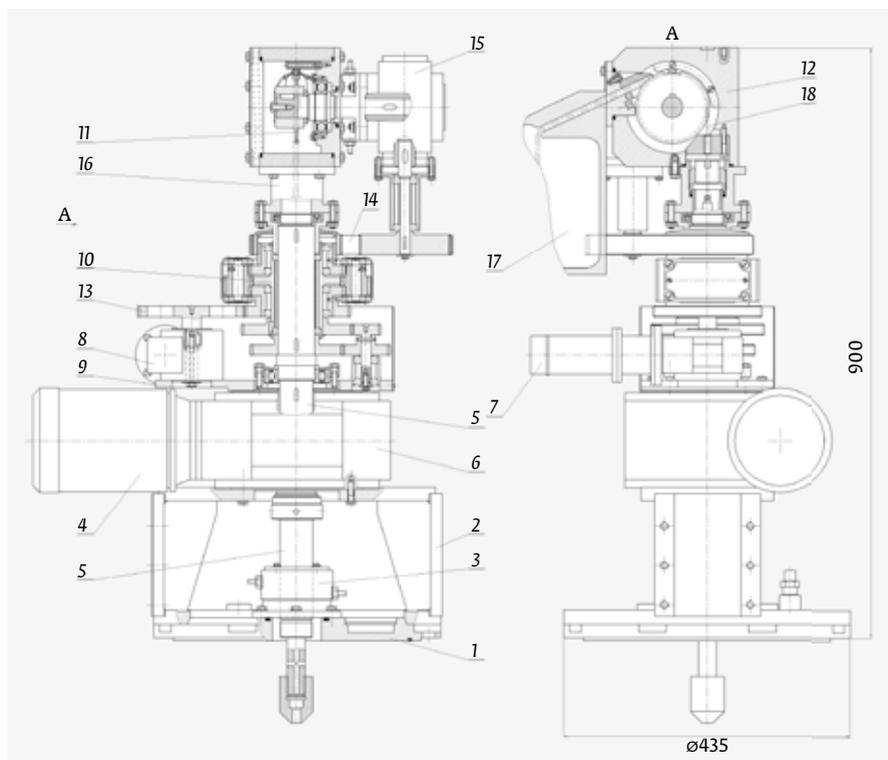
Конструкция привода вращения и перемещения затравки для установок выращивания монокристаллов кремния. 1 – крышка; 2 – подставка; 3 – вакуумный ввод; 4 – мотор-редуктор; 5 – шток; 6 – редуктор; 7 – серводвигатель; 8 – редуктор червячный; 9 – плита; 10 – дифференциал; 11 – звездочка; 12 – лебедка; 13 – пара шестерен; 14 – зубчатая ременная пара; 15 – редуктор червячный; 16 – переходник; 17 – магазин; 18 – цепь
